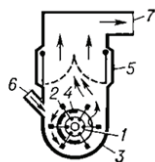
Помольный комплекс ударного действия: 1 — ротор; 2 — било; 3 — кожух; 4 — патрубок для горячего воздуха; 5 — шахта; 6 — загрузочный желоб; 7 — разгрузочный газосход.
